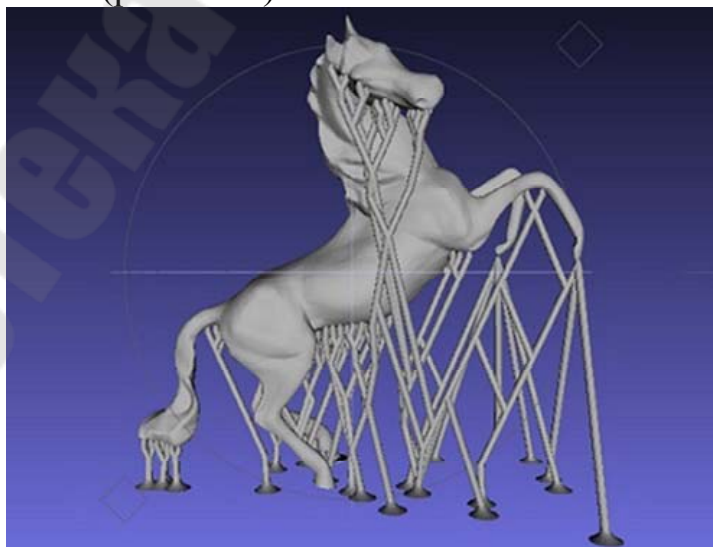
Цифровая модель с поддерживающими конструкциями
